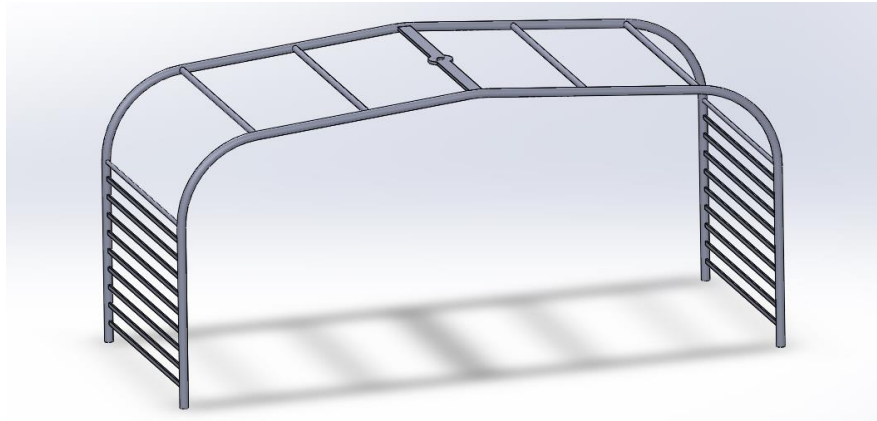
Vista en planta de la estructura con la barra rectangular central. Fuente: Propia.
